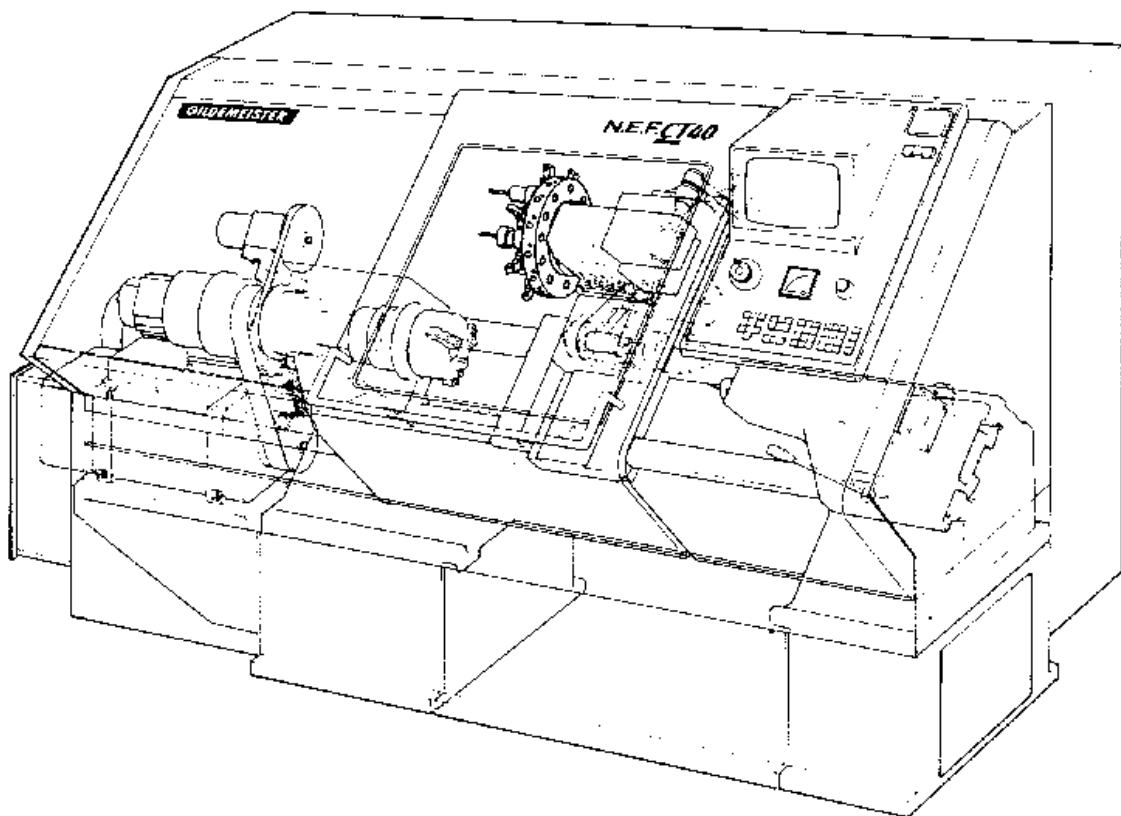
Direktantrieb der Hauptspindel bei einer CNC – Drehmaschine
